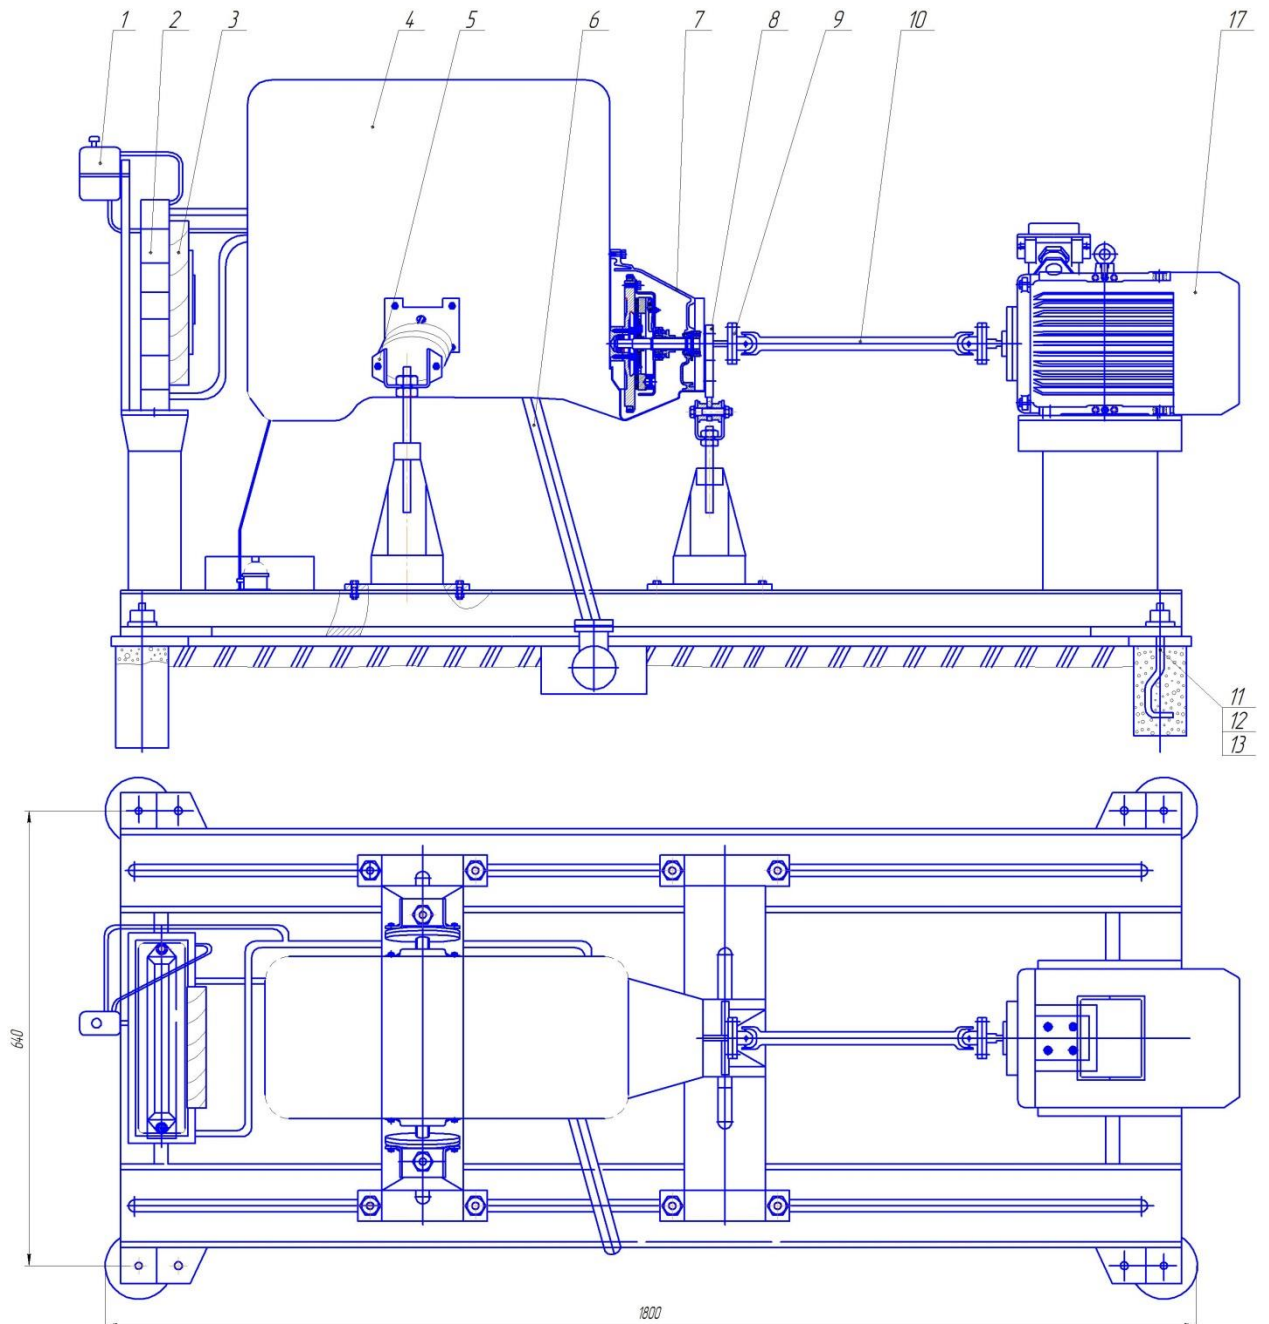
Устройство стенда для обкатки двигателя легкового автомобиля
